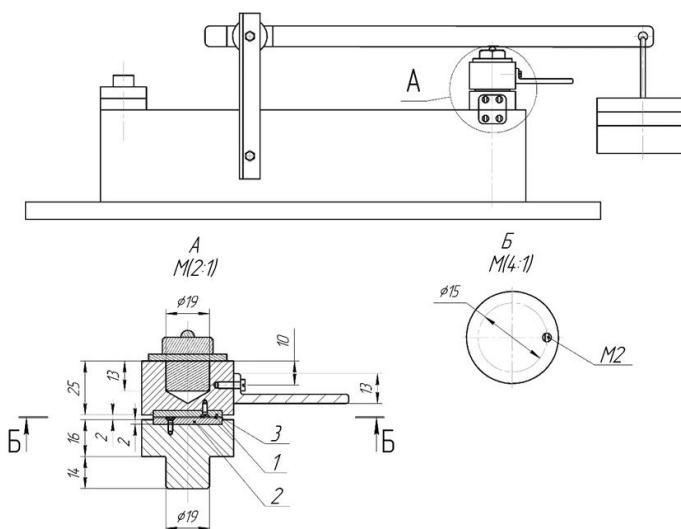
Схема приспособления для исследования образцов на способность шаржирования абразива в материал: 1 - свободный абразив; 2 – исследуемый образец; 3 - образец из меди
